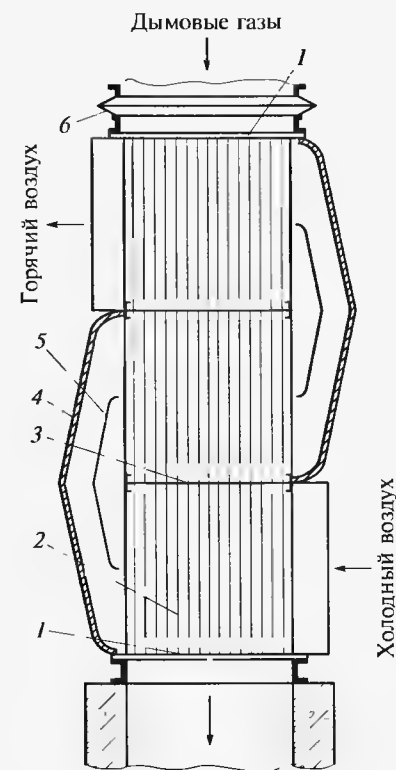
Воздухоподогреватель рекуперативного типа:
